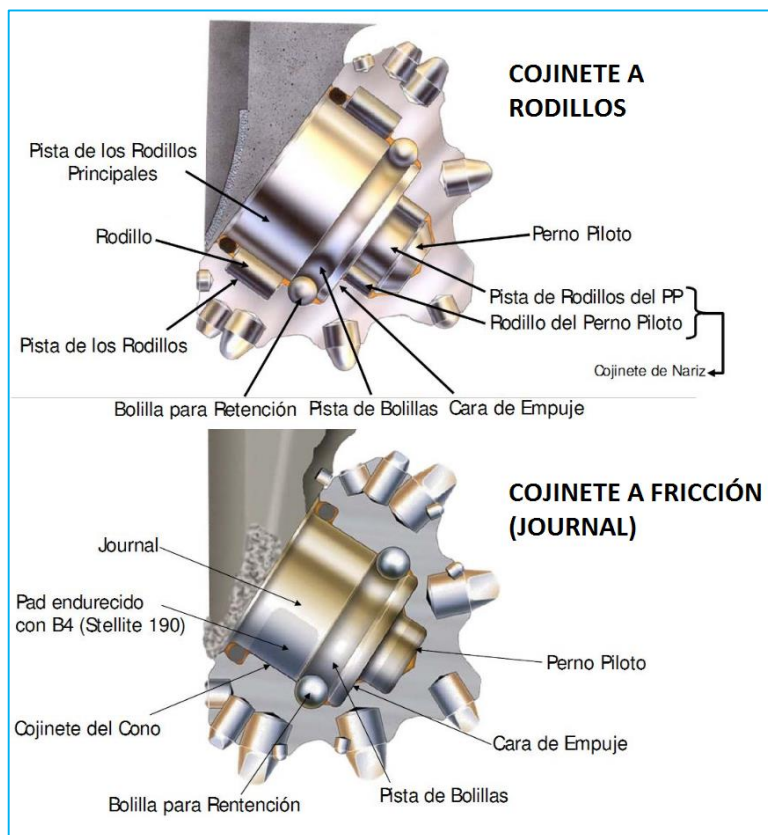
Componentes de Cojinetes a Rodillos y a Fricción (Journal) de Brocas Tricónicas.
